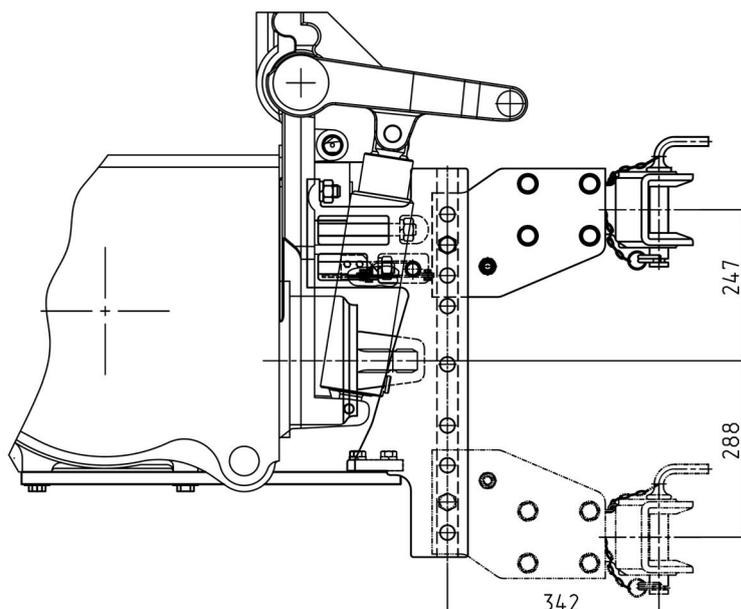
Schéma des variantes d'installation du dispositif TSU-3V (fourche longue de traction)
